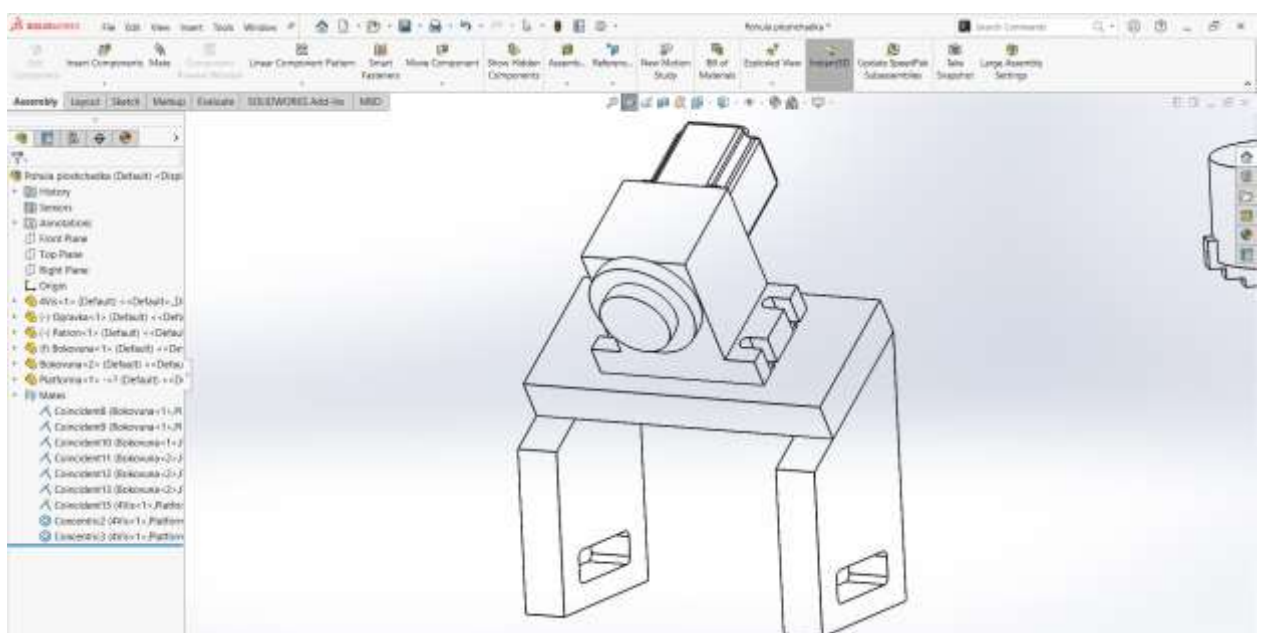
Розташування поворотного механізму на похилій платформі
